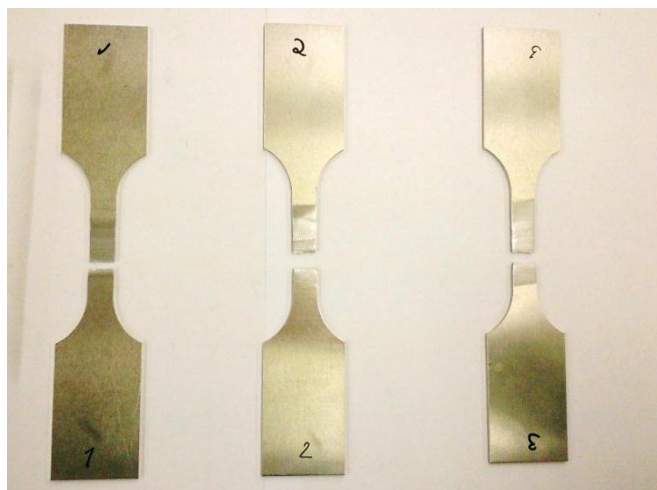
Образцы сварных листов рабочего участка, вырезанные из сварного соединения для испытания на растяжение
